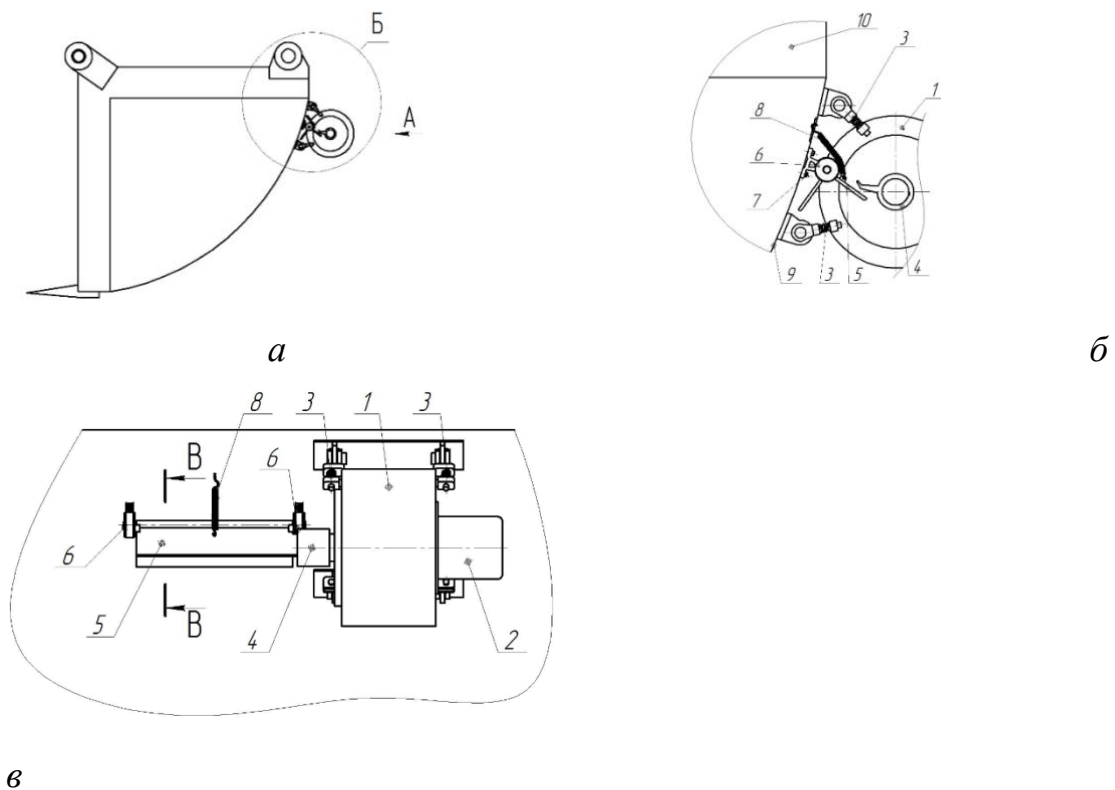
Пристрій для очищення ковша від ґрунту: *а* – загальний вид; *б* – збільшено вид Б; *в* – вид А; 1 – планетарний редуктор; 2 – електродвигун; 3 – опорні елементи; 4 – ексцентрик; 5 – важільний ударник; 6 – підшипникові опори; 7 – болтове з’єднання; 8 – пружина; 9 – задня стінка; 10 – ківш
